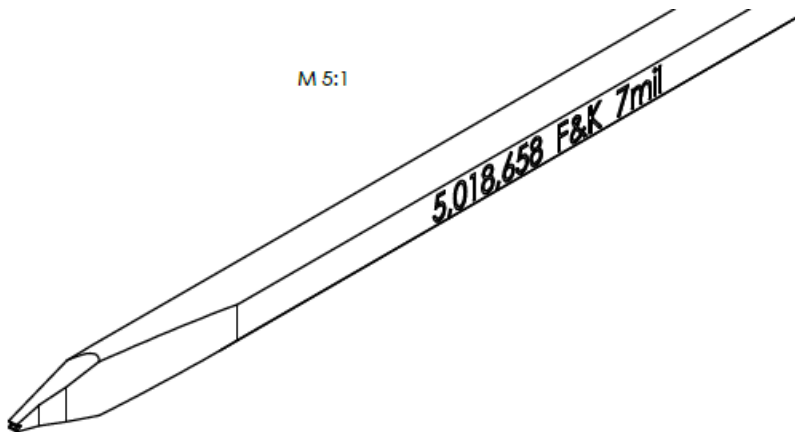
Typisches Dickdraht-Bondwerkzeug von 50 mm Länge
